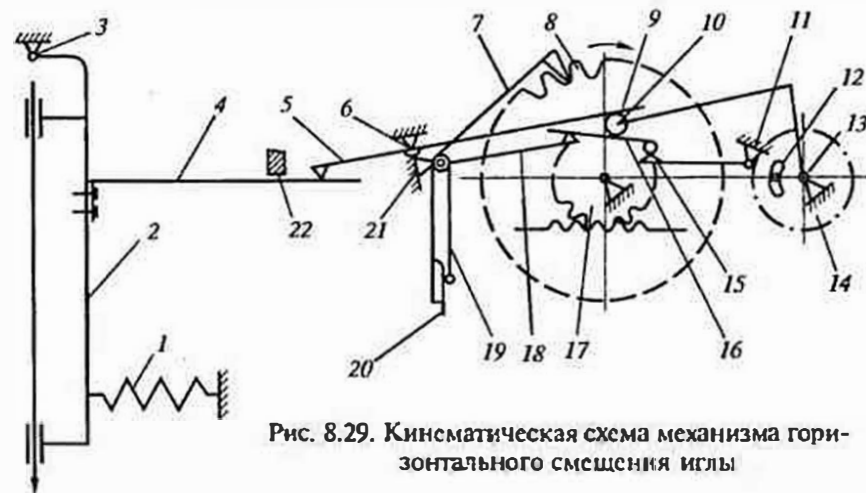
Кинематическая схема механизма горизонтального смещения иглы
